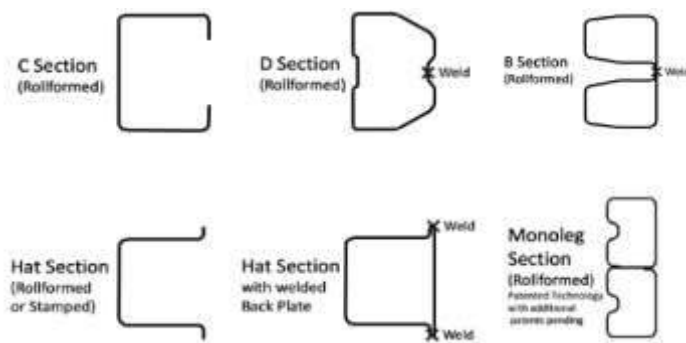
Secciones Transversales de la viga de refuerzo.
